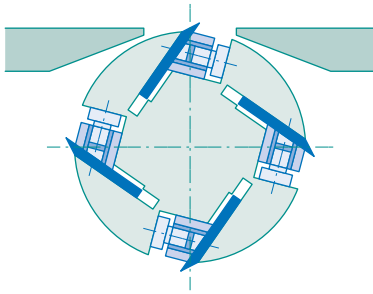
Vue en coupe d'un porte-outil suivant un plan perpendiculaire à l'axe de rotation - *Cross-sectional view of a tool holder along a plane perpendicular to the axis of rotation
